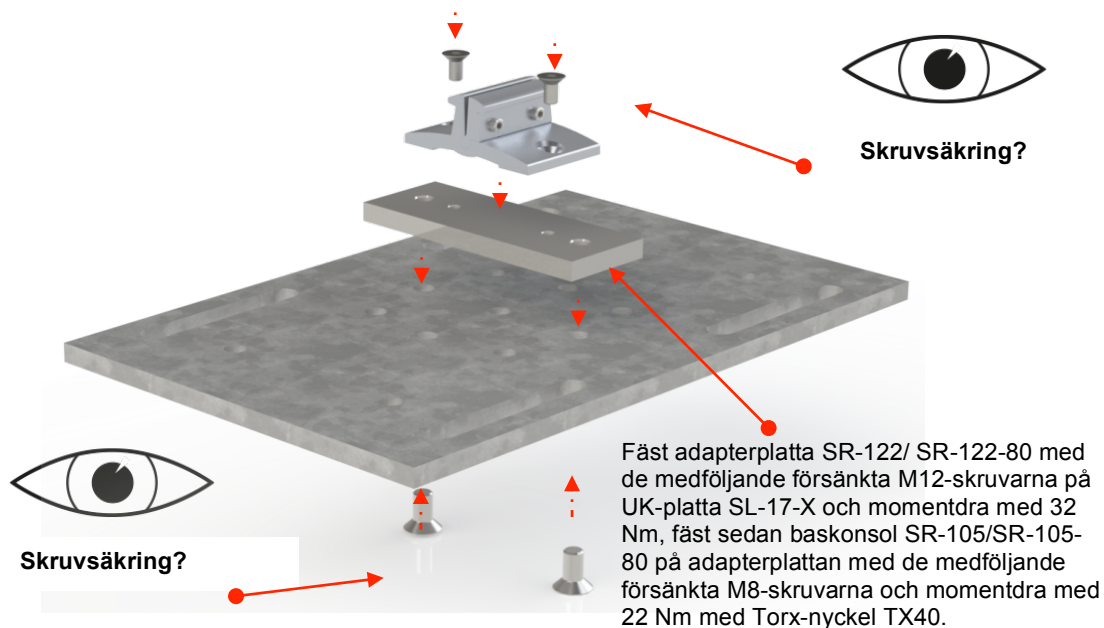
Montering av baskonsol SR-105 på adapterplatta SR-122 för UK-plattor SR-017
